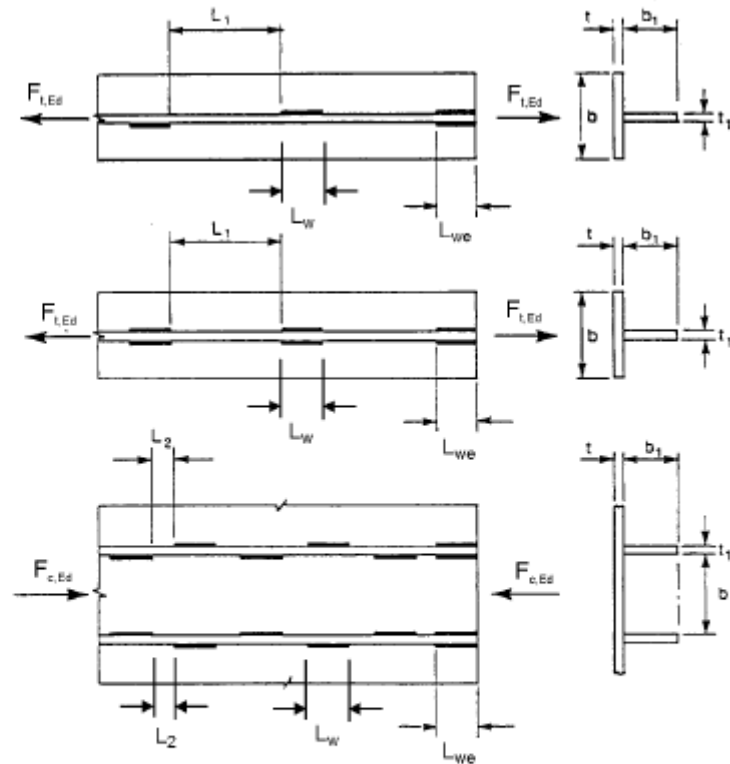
Soldadura de ângulo descontínua [17]
